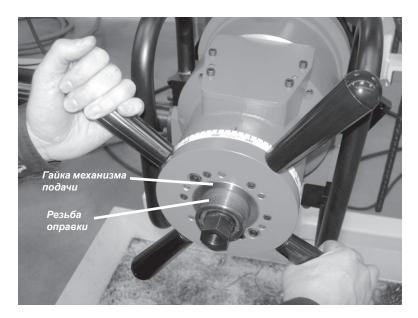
Поверните ручку подачи по часовой стрелке для сцепления резьбы оправки с гайкой механизма подачи.
